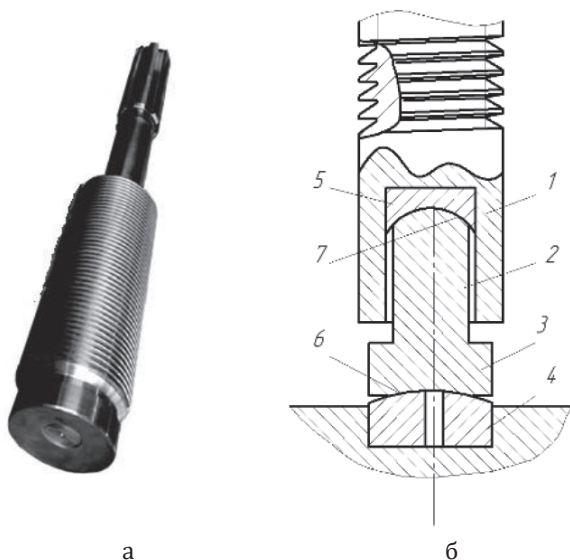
Гвинт та опора натискного механізму прокатного валка
